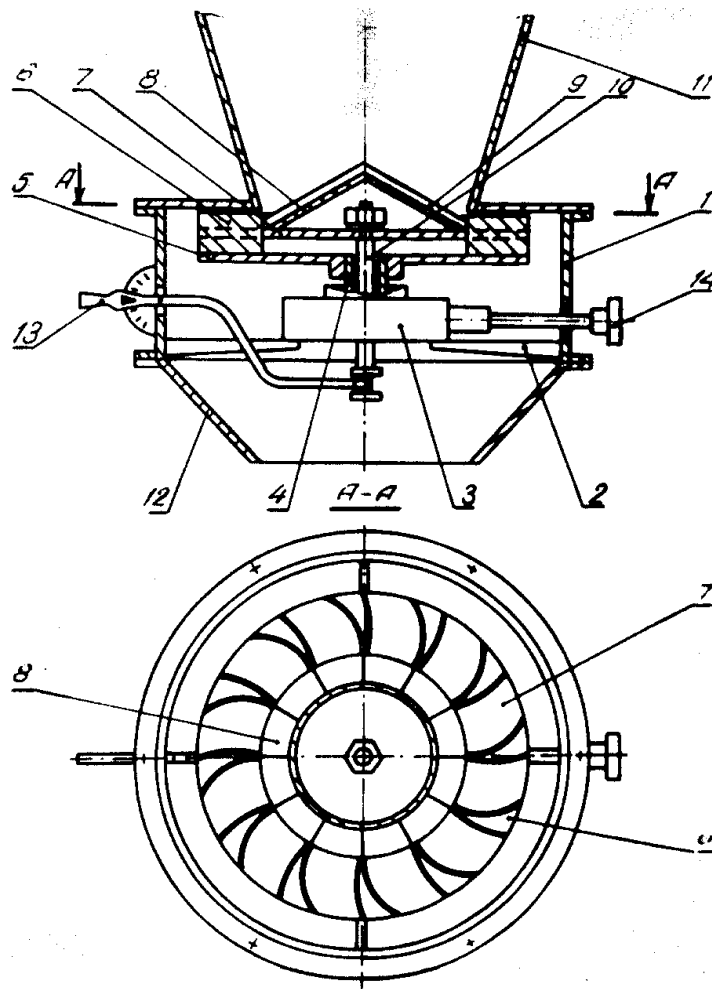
Конструктивна схема ротаційного дозатора: 1 – корпус; 2 – кронштейни; 3 – редуктор; 4 – трубчатий вал; 5 – дозуючий диск; 6 – направляючі елементи; 7 – рухоме дно; 8 – подаючий конус; 9 - лопаті; 10 - рухомий вал; 11 – наддозаторний бункер; 12 – збиральний конус; 13 – регулювальна ручка; 14 – приводний вал редуктора
